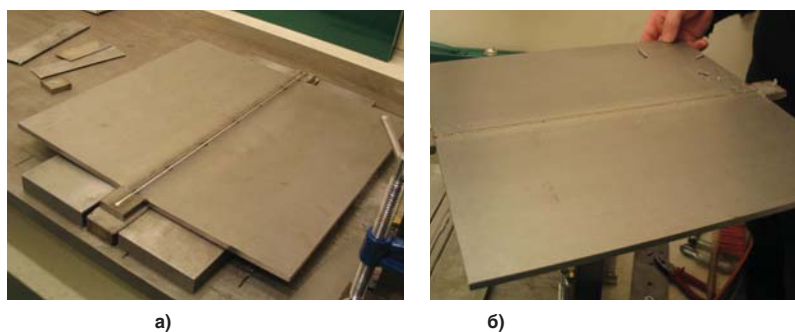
Внешний вид контрольной планки после лазерной сварки на флюсовой подушке со стороны лицевого (а) и обратного (б) валиков сварного соединения.
